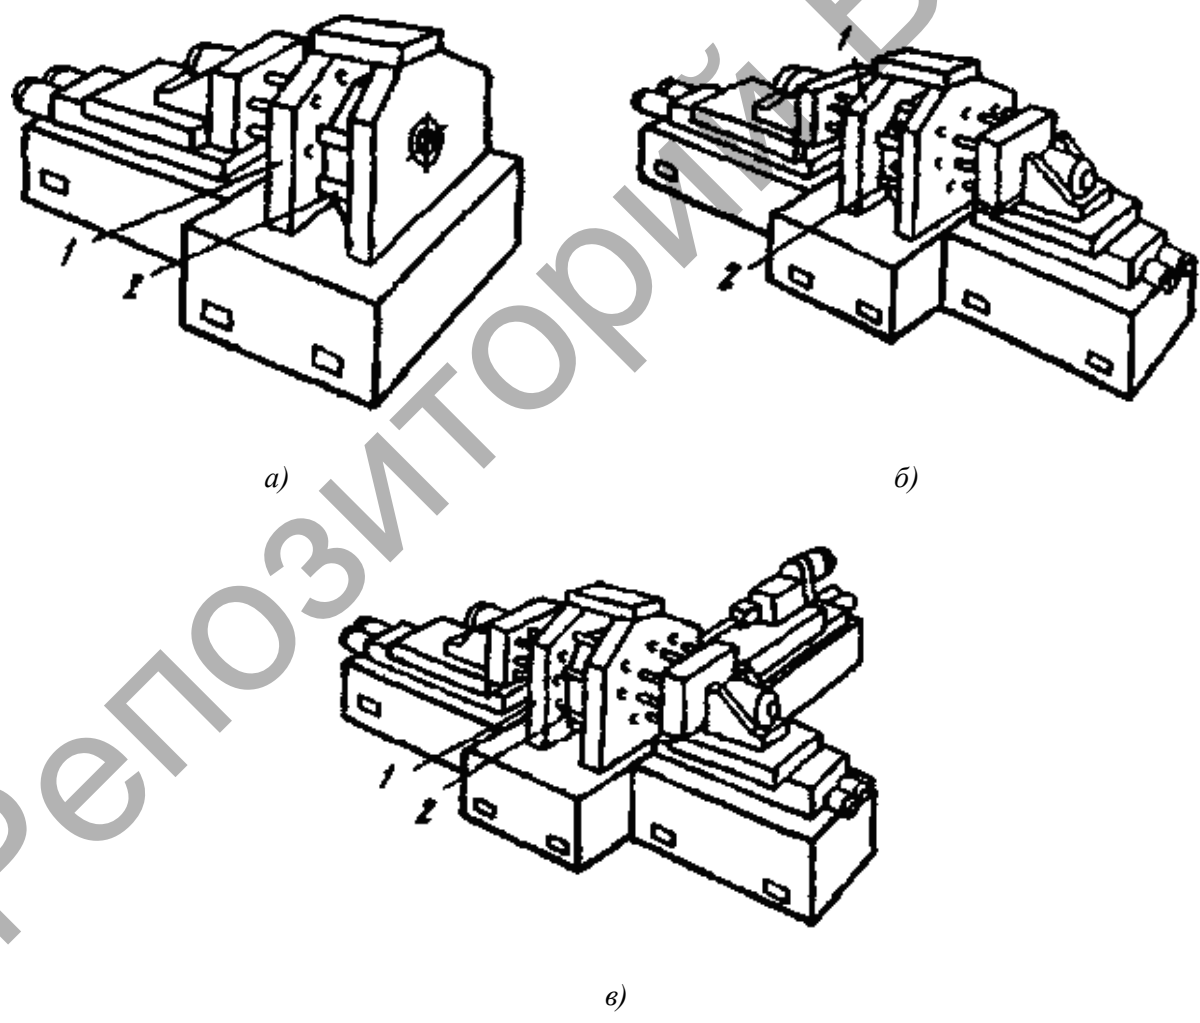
Типовые компоновки агрегатных станков с поворотным делительным барабаном
